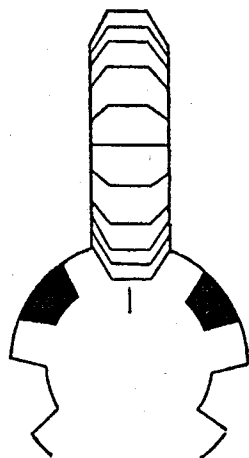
Установка фрезы при фрезеровании шлицевых валов
